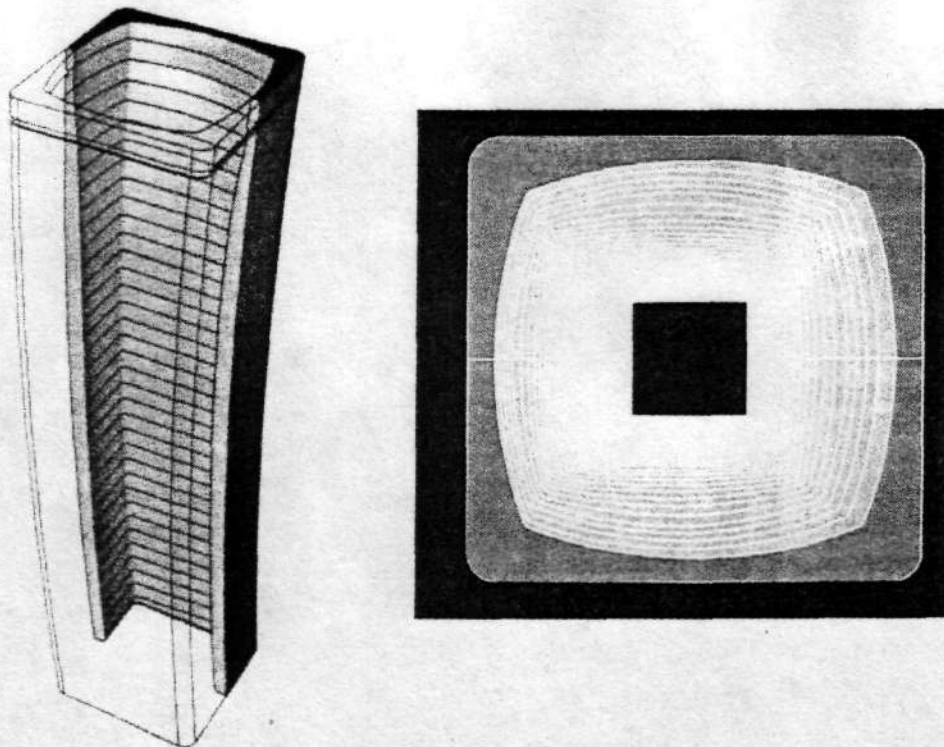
Общий вид, профиль (слева) и вид сверху (справа) гильзы кристаллизатора конструкции "Convex Mould"
